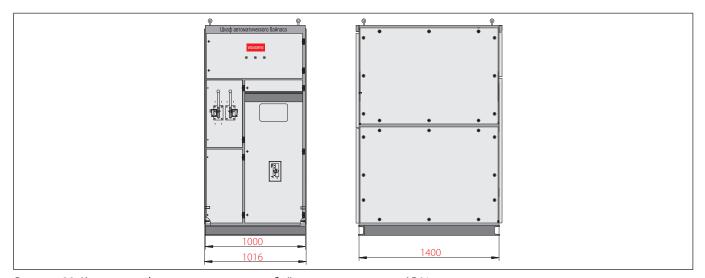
Корпус шкафа автоматического байпаса типоразмера АВО1
